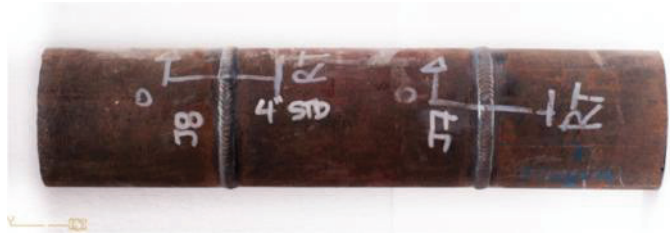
Cupón de prueba soldado 4" SCH STD- Proceso GTAW
